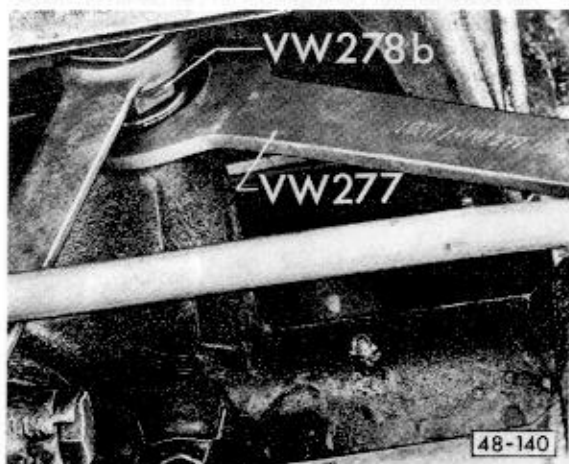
Kontermutter für Nachstellschraube lösen
